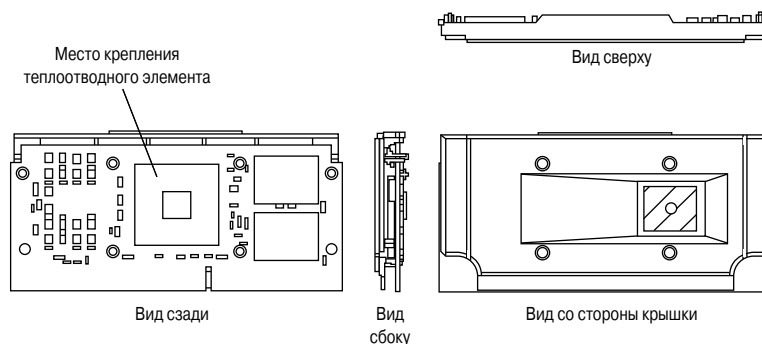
Корпус SECC2 процессоров Pentium II/III
